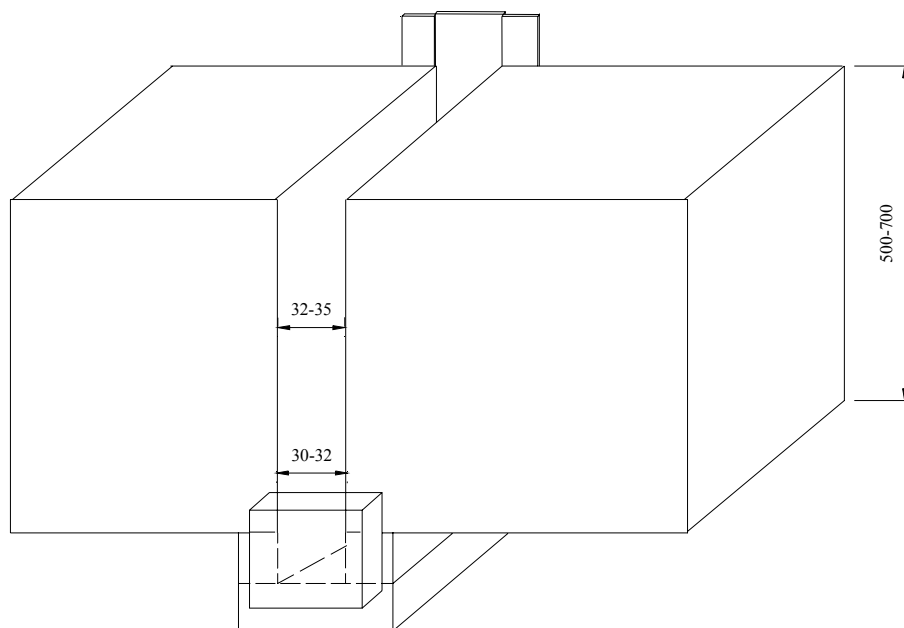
Схема сборки всех образцов и деталей при сварке
